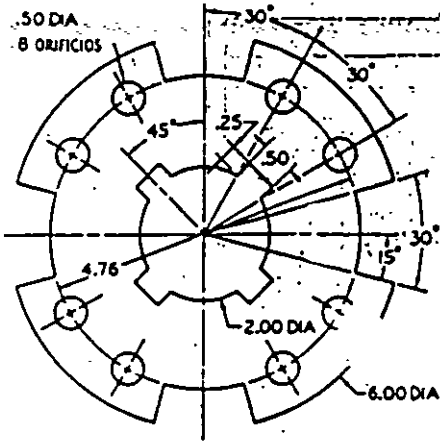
Placa de fricción. Usando el plan A-2, trácelo a lápiz. Omíta dimensiones y notas.
